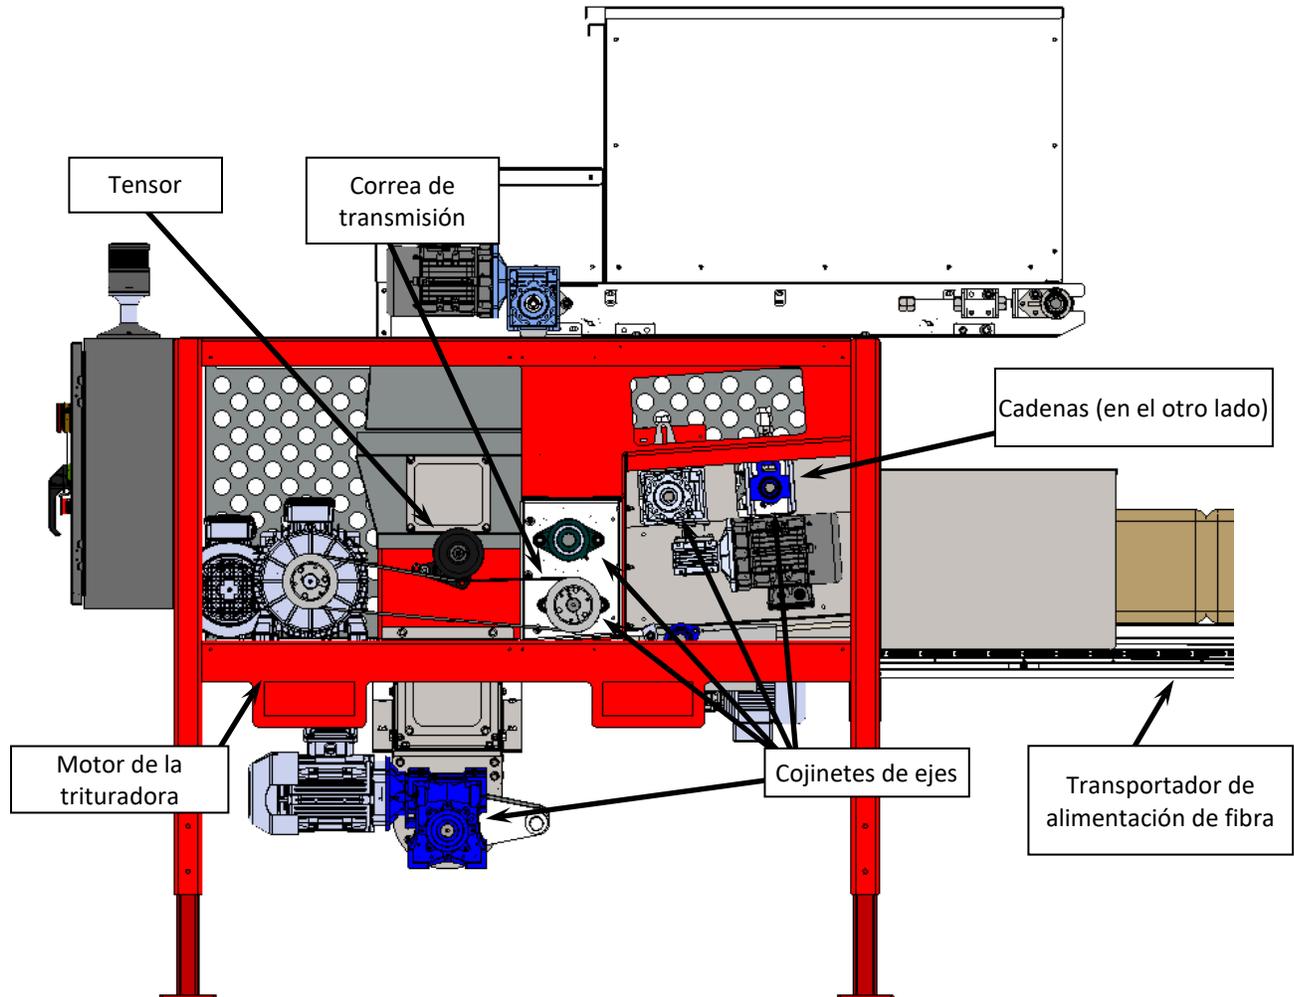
Figura B. Lado izquierdo de la máquina (el lado derecho es similar)
